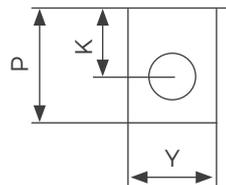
BQ3A-125-800 开关本体外形尺寸和安装尺寸
